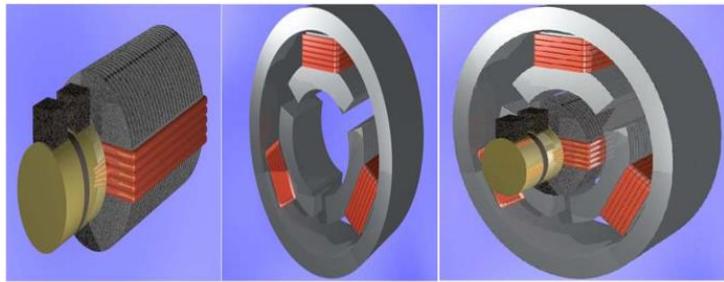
b. La structure des machines à induit fixe est inducteur tournant
